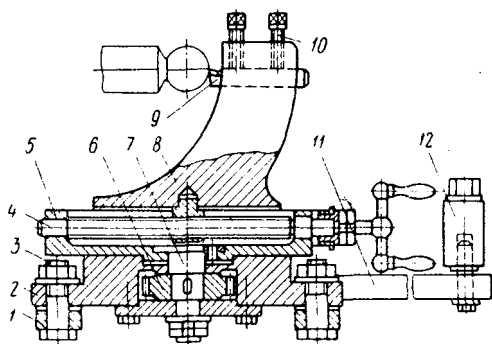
Приспособление к токарным станкам для обработки наружных и внутренних поверхностей диаметром от 20 до 200 мм
